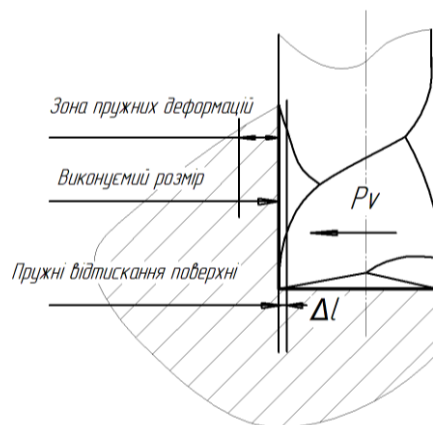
Схема силової взаємодії кінцевої фрези та матеріалу заготовки з пластмаси з урахуванням пружних відтискань
